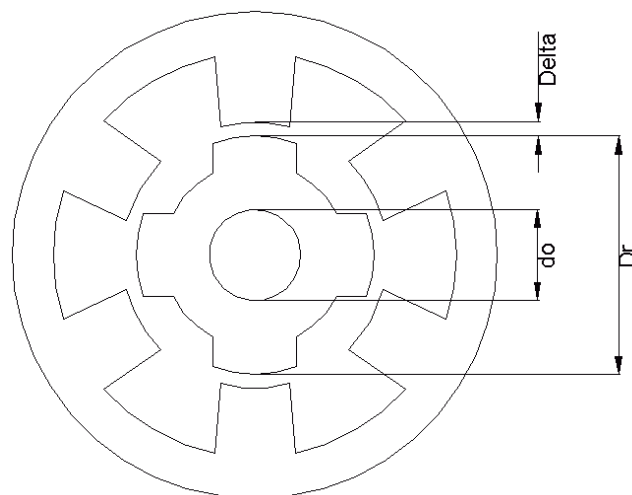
Размеры: диаметр вала, диаметр ротора и воздушный зазор, для трехфазного ВРД конструкции 6/4
